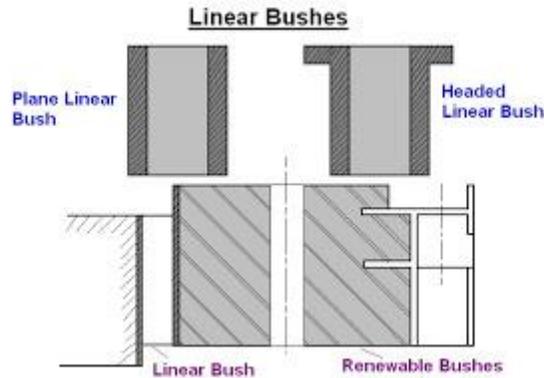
Linear Bushes. Fuente: American Machinist
